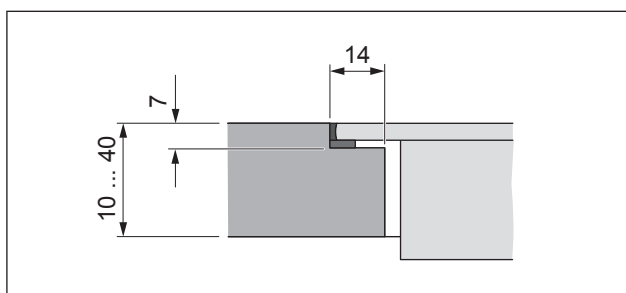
Dimensione dell'incassatura per montaggio a filo piano
